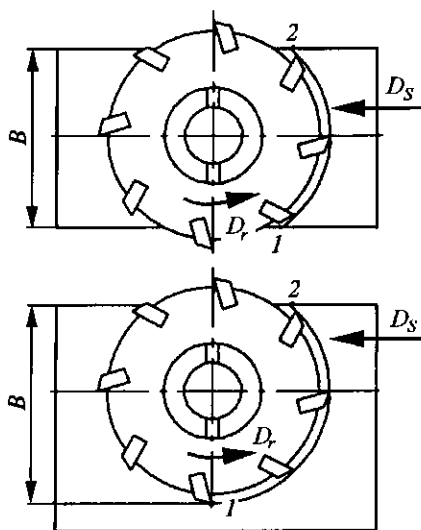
Схемы фрезерования при работе торцовыми фрезами
